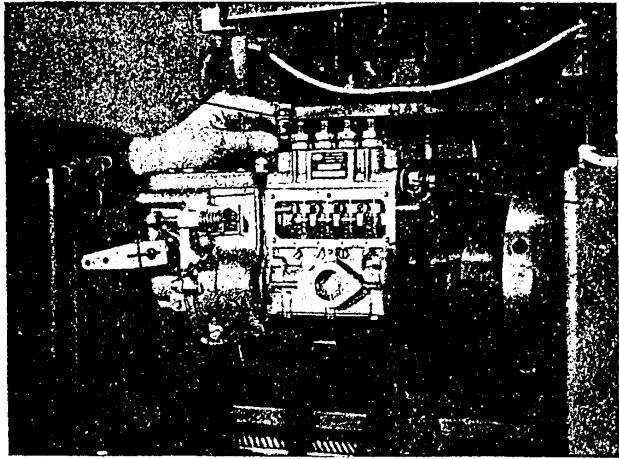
Einspritzpumpe auf dem Prüfstand anschließen
